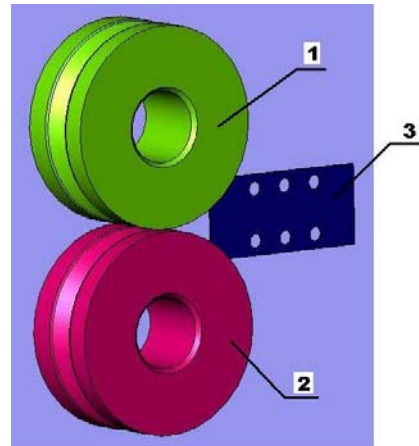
Роликовый калибр для изготовления профиля уголкового типа: 1 – верхний ролик; 2 – нижний ролик; 3 – заготовка
